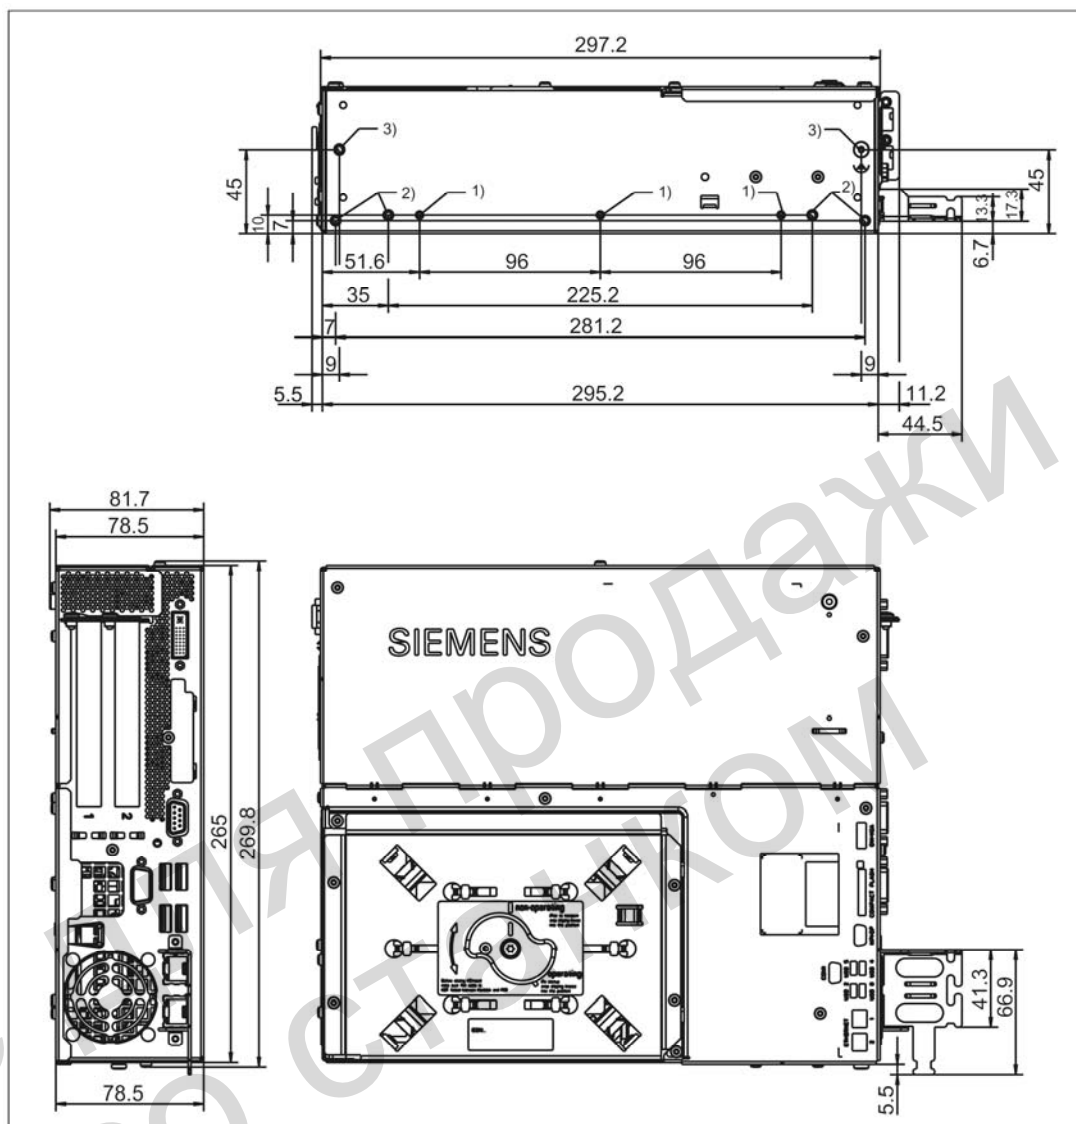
PCU 50.3 габаритный чертеж для монтажа с разгрузкой от натяжения ЕТН
